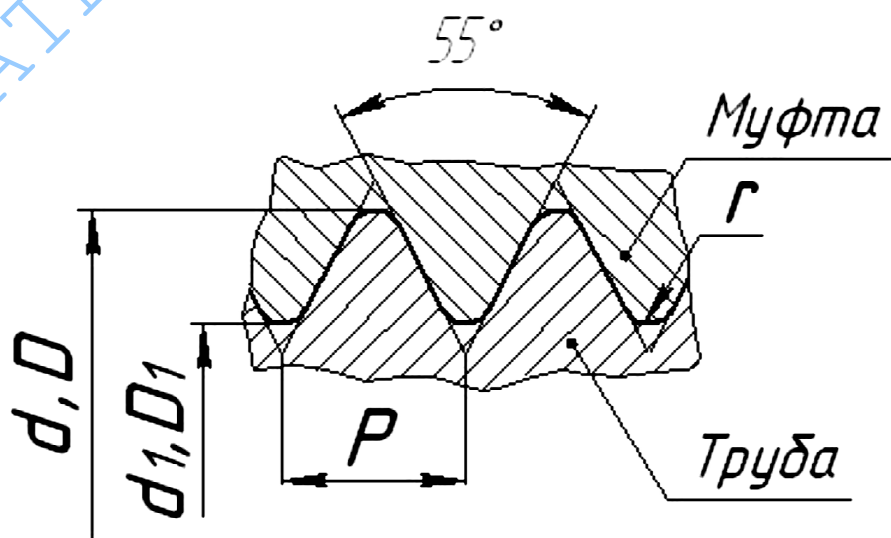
Резьба трубная коническая (ГОСТ 6211-81)
